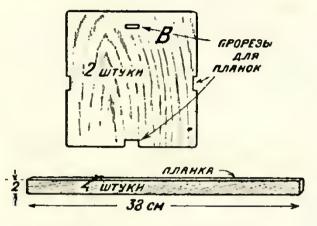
Вверху: вид боковины; внизу: размеры плаики.
